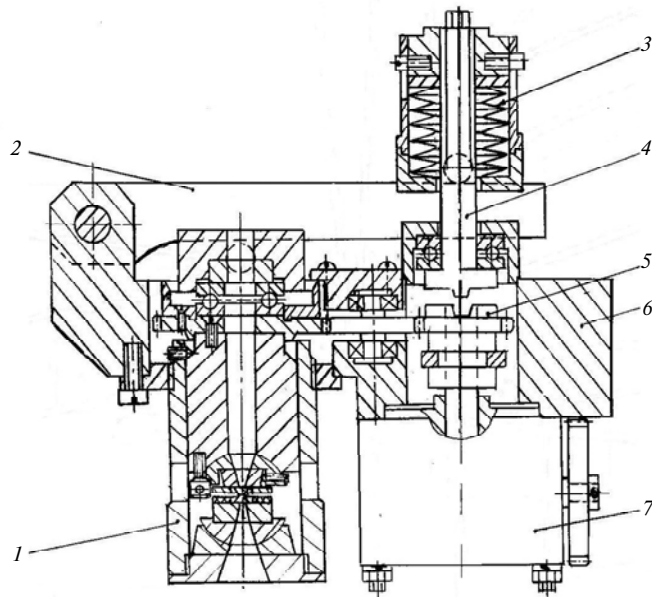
Схема SDAC с нагружающим устройством: 1 – SDAC; 2 – рычаги; 3 – тарельчатые пружины; 4 – ось; 5 – переключающее устройство; 6 – корпус; 7 – редуктор.
